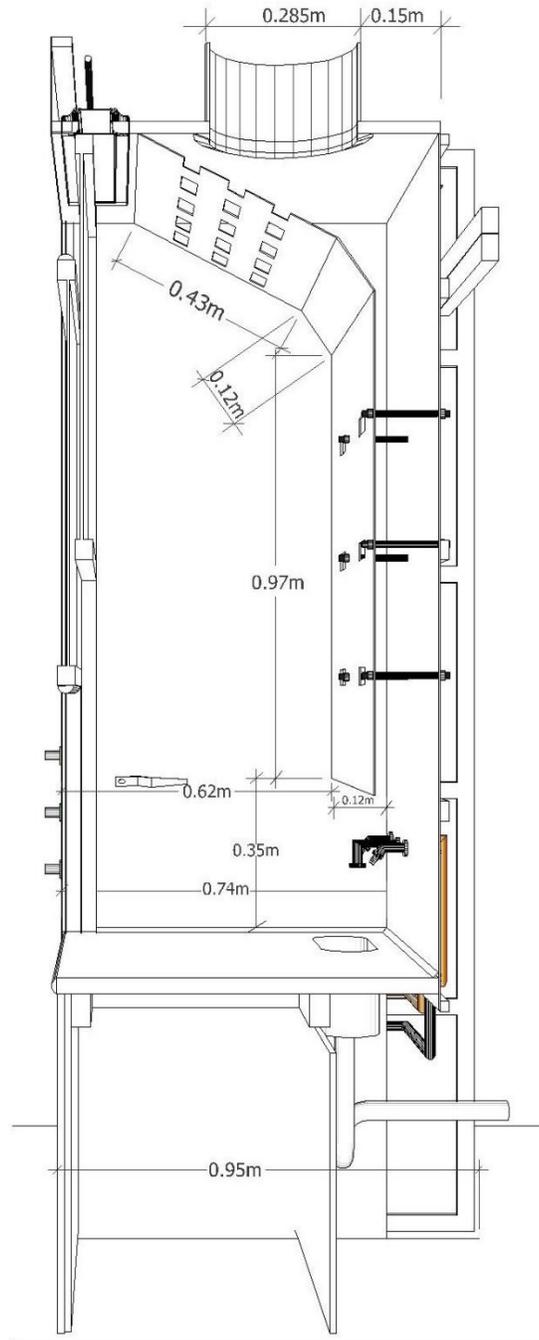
Campana de extracción VAV modelo 1 800. Vista con dimensiones en altura y largo en plano frontal.
